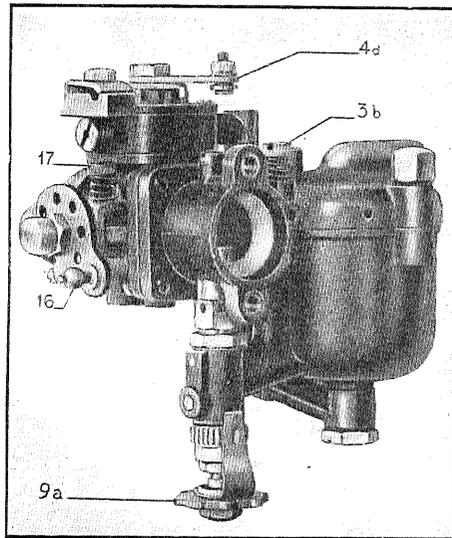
Carburatore senza raccordo del filtro d'aria.
